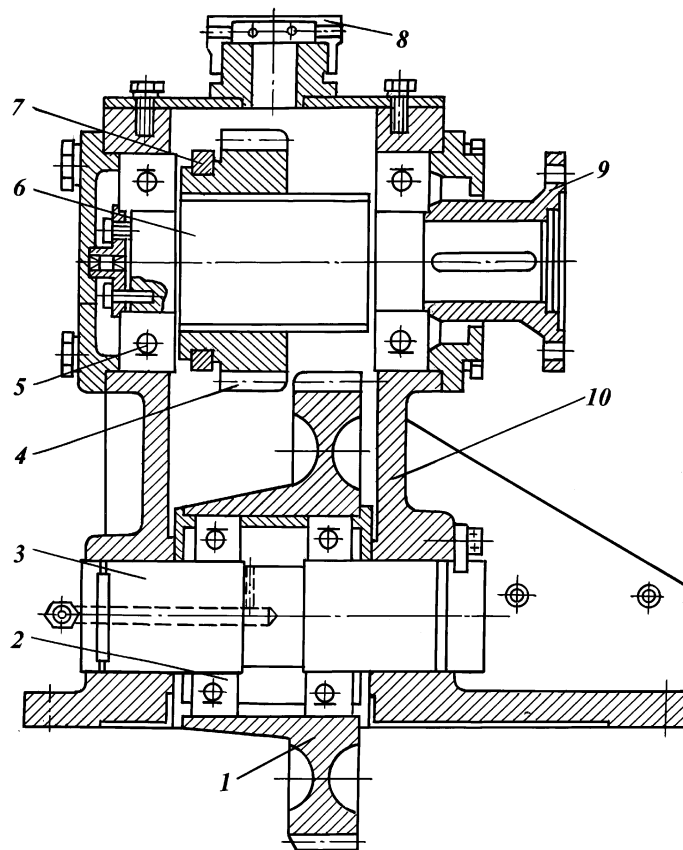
Коробка отбора мощности для привода компрессора установки УС5-30:
